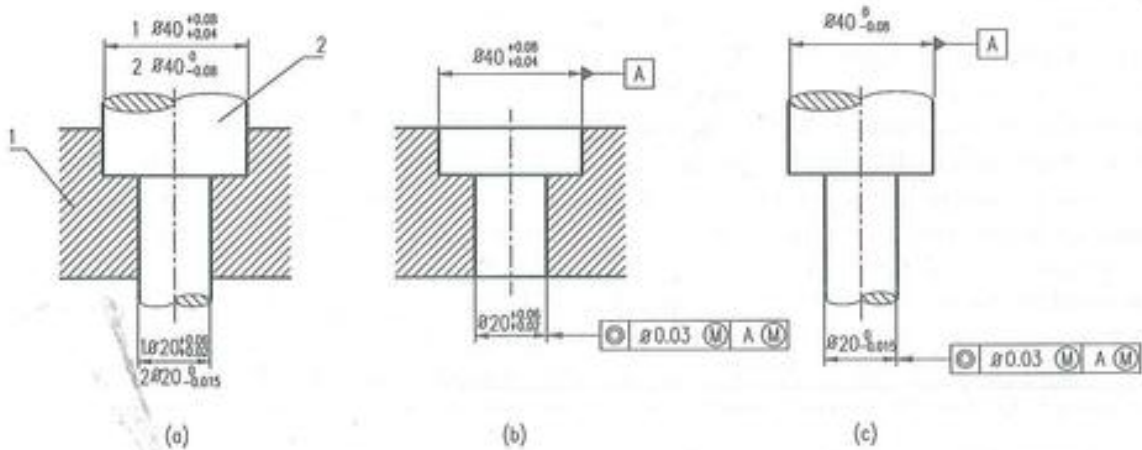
Combinación de ajustes y tolerancias geométricas de perpendicularidad.
